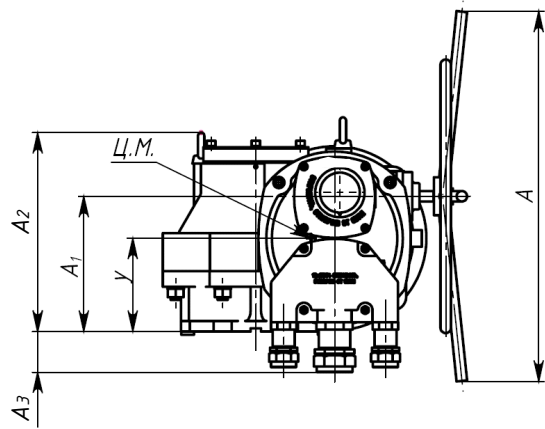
г – Габаритные размеры привода конструктивной схемы 43
